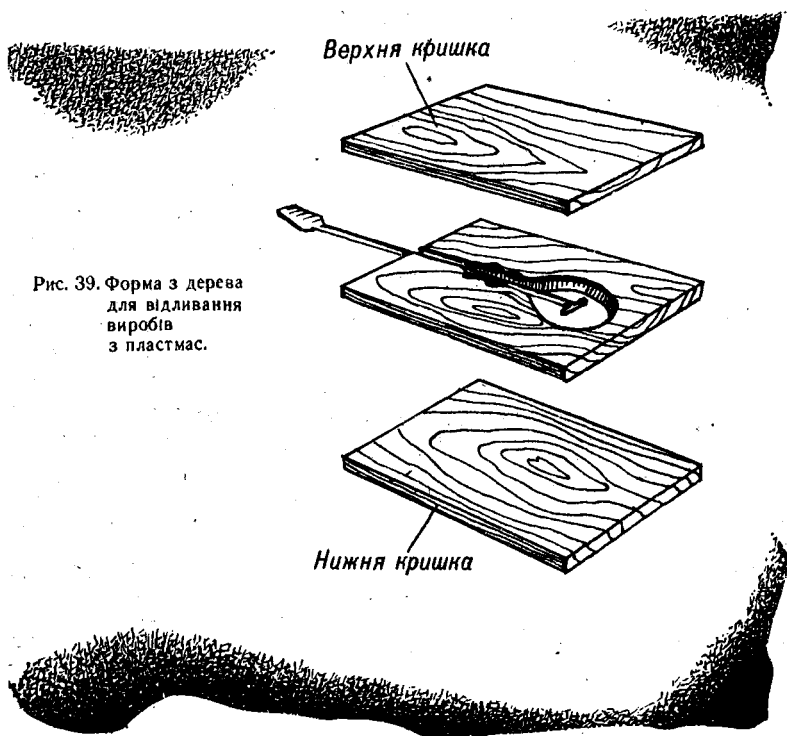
Форма з дерева для відливання виробів з пластмас.
